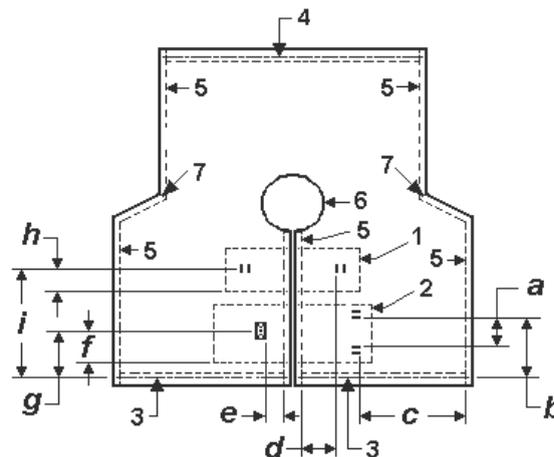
Conjunto de tira pectoral (parte ajustable izquierda y parte fija derecha)
